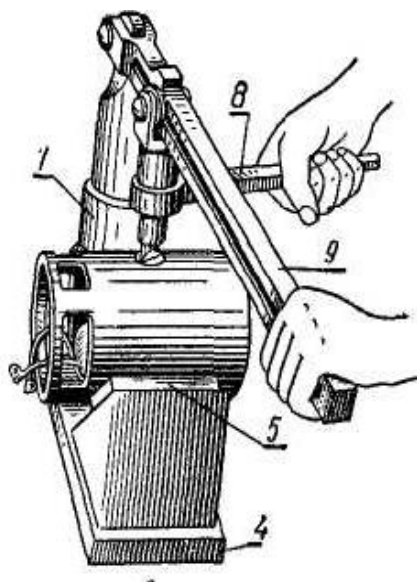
Рычажное приспособление для откручивания винтов
